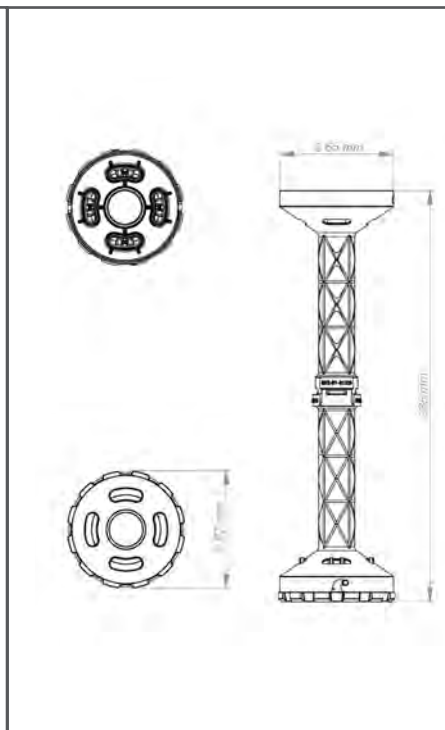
Ansicht Innenteil Magnetflussfilter
